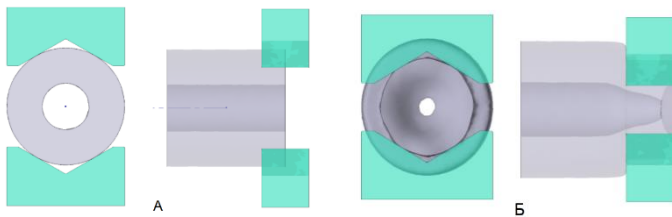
Моделювання кування циліндра з наскрізним отвором, А – початкова заготовка, Б – поковка
